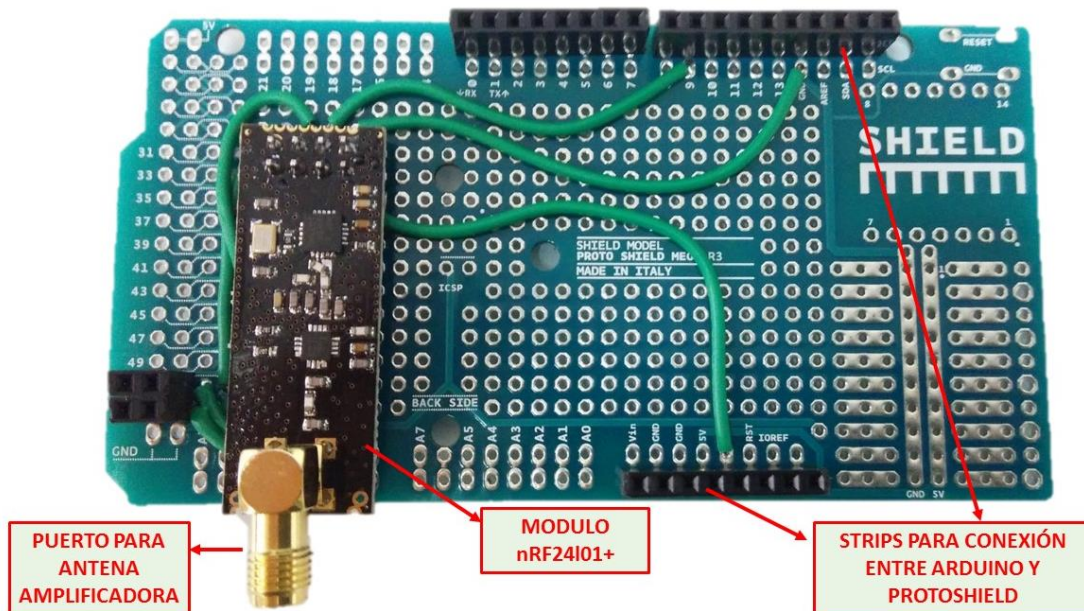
Vista interior del protoshield con cableado, modulo RF y strips soldados (Fuente: propia)
